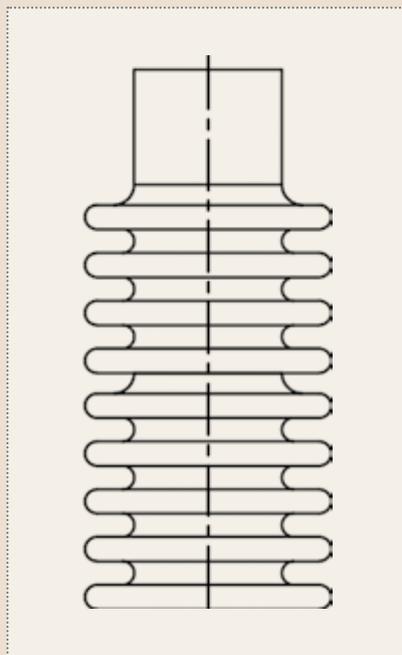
Пример сильфона из трубки со сварным швом
